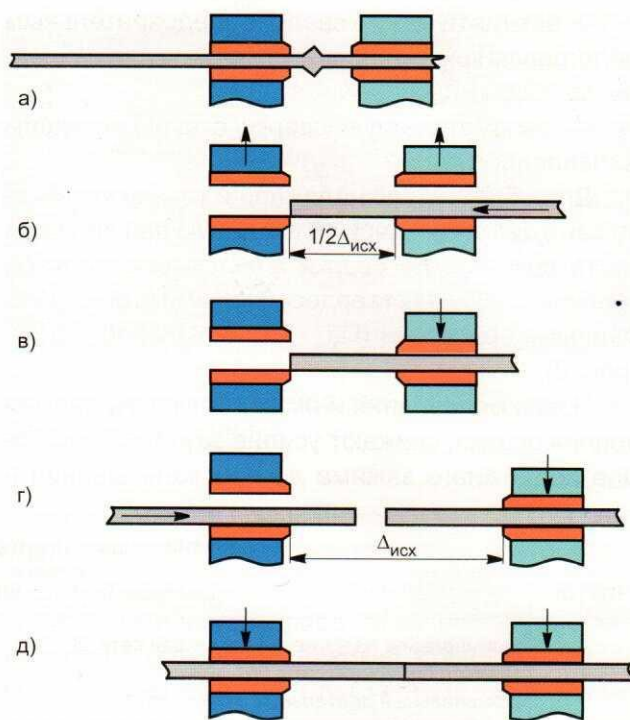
Схема положения зажимных электродов машины при полуавтоматической установке заготовок под сварку: а) после сварки предыдущего стыка заготовок; б) после подъема электродов и отвода подвижного до половины исходного расстояния и подачи до упора первой заготовки; в) после зажима первой заготовки в подвижных электродах; г) после отвода подвижных электродов с зажатой заготовкой до исходного расстояния перед сваркой; д) после подачи второй заготовки до упора в первую и зажима второй заготовки в неподвижных зажимах
